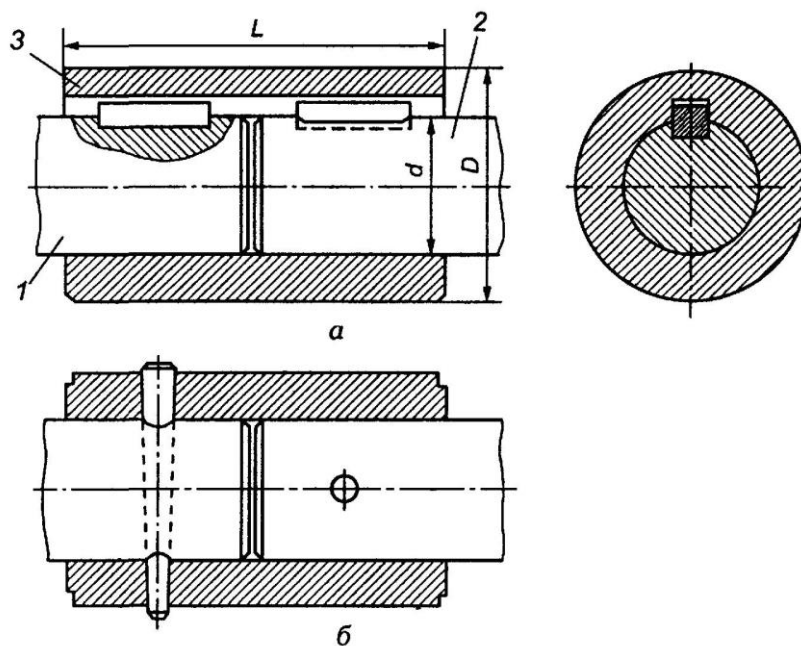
Втулочная муфта: а — крепление на шпонке; б — крепление штифтом
